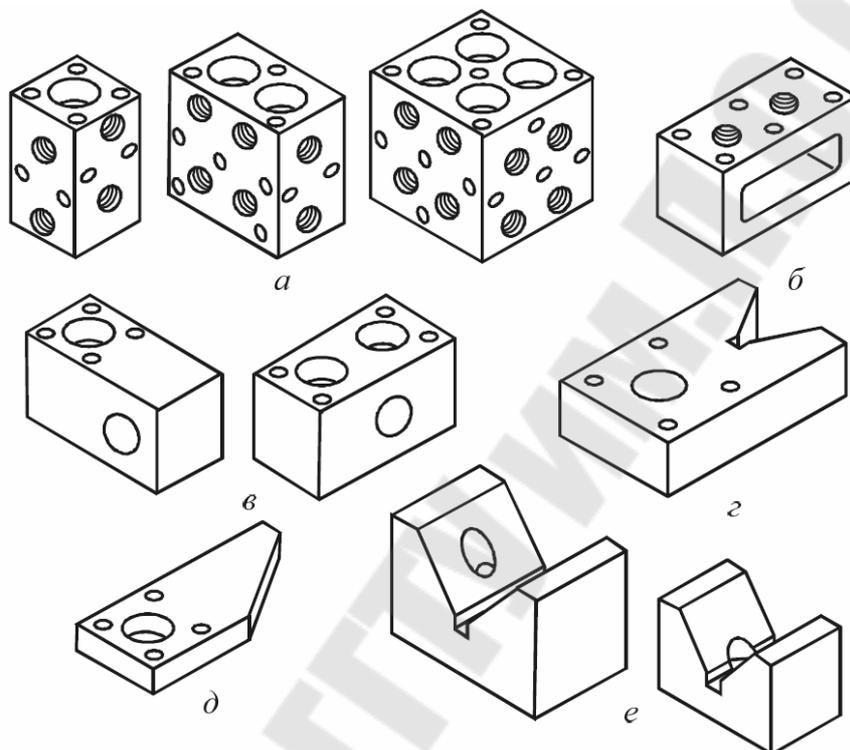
Типовые корпусные детали универсально-сборной переналаживаемой оснастки [4]
